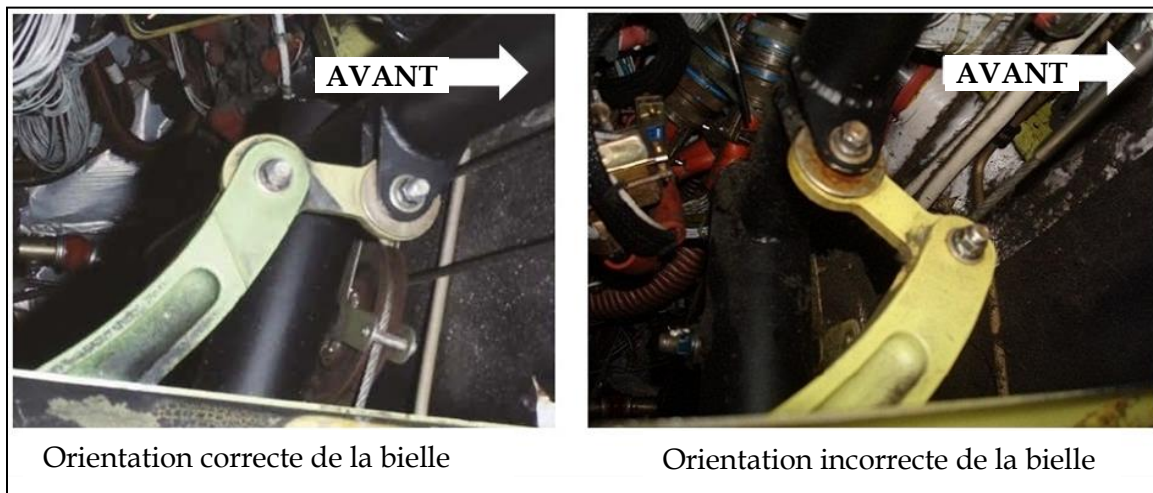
Couplage à bielle du contrepoids d'équilibrage
